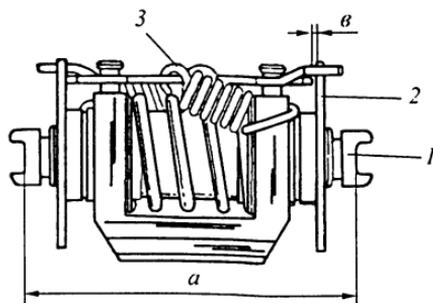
Механизм автоматической установки тормозных колодок фирмы Perrot: a — установочный размер; b — зазор; 1 — регулировочные винты; 2 — установочное зубчатое колесо; 3 — натяжная пружина
